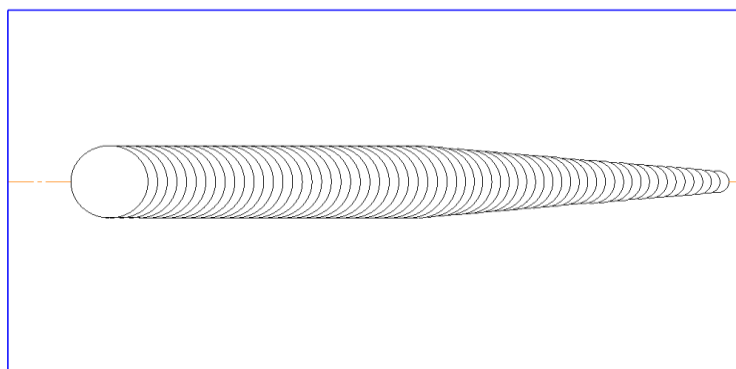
Эскиз сварного соединения при использовании способов уменьшения размеров сварочного кратера.
